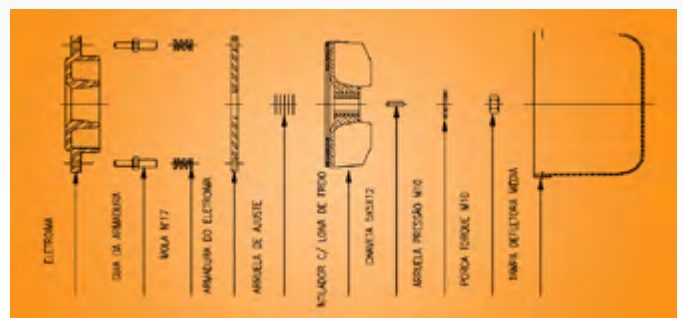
Detalhamento do sistema de freio do motor. Fonte: Adaptado de CSM 2021
